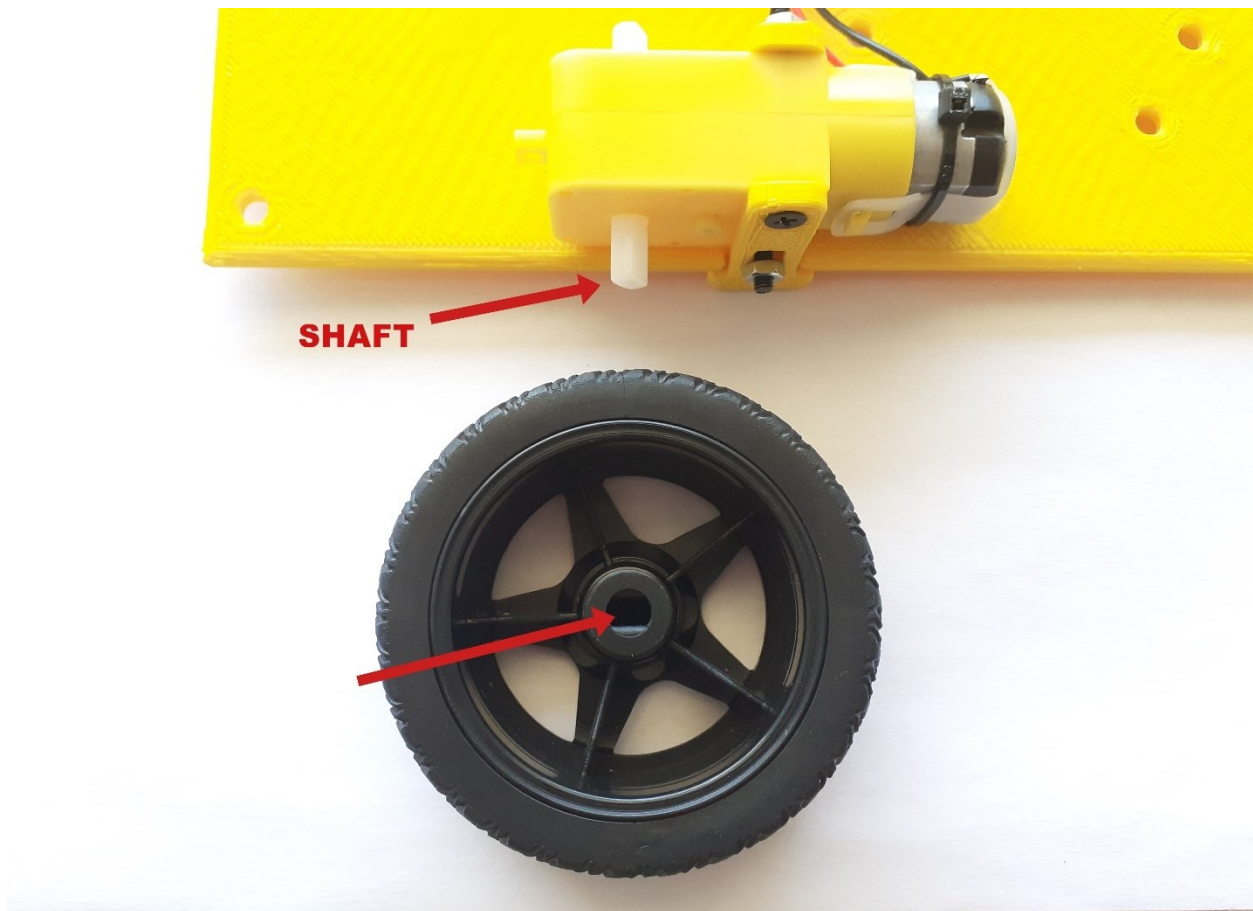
Comment clipser la roue sur le moteur à engrenages DC
